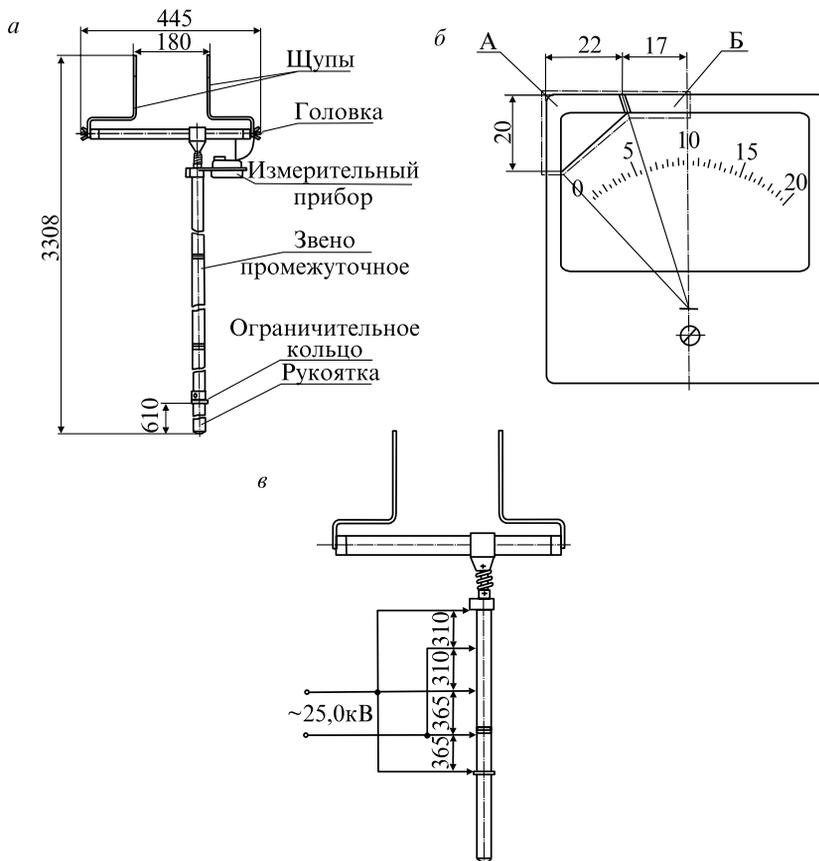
Штанга ШДН-27,5 кВ для дефектировки изоляторов контактной сети переменного тока: *а* — общий вид штанги; *б* — измерительный прибор; *в* — схема проверки исправности штанги
